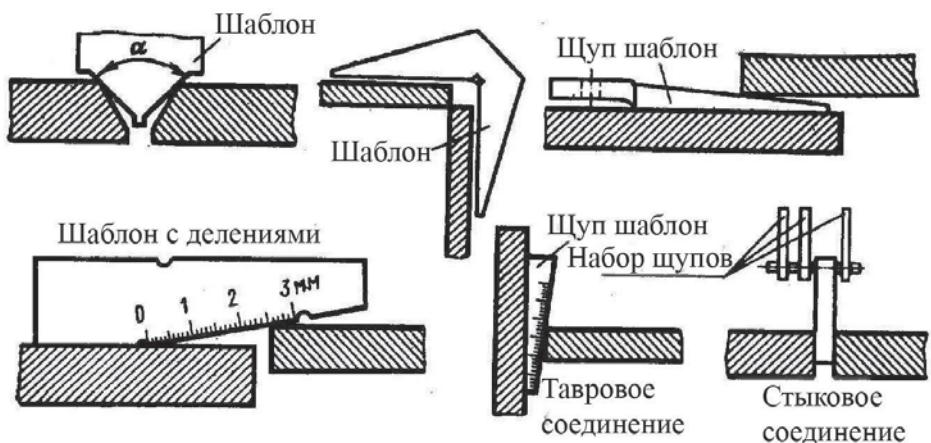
Контроль качества сборки с помощью шаблонов
